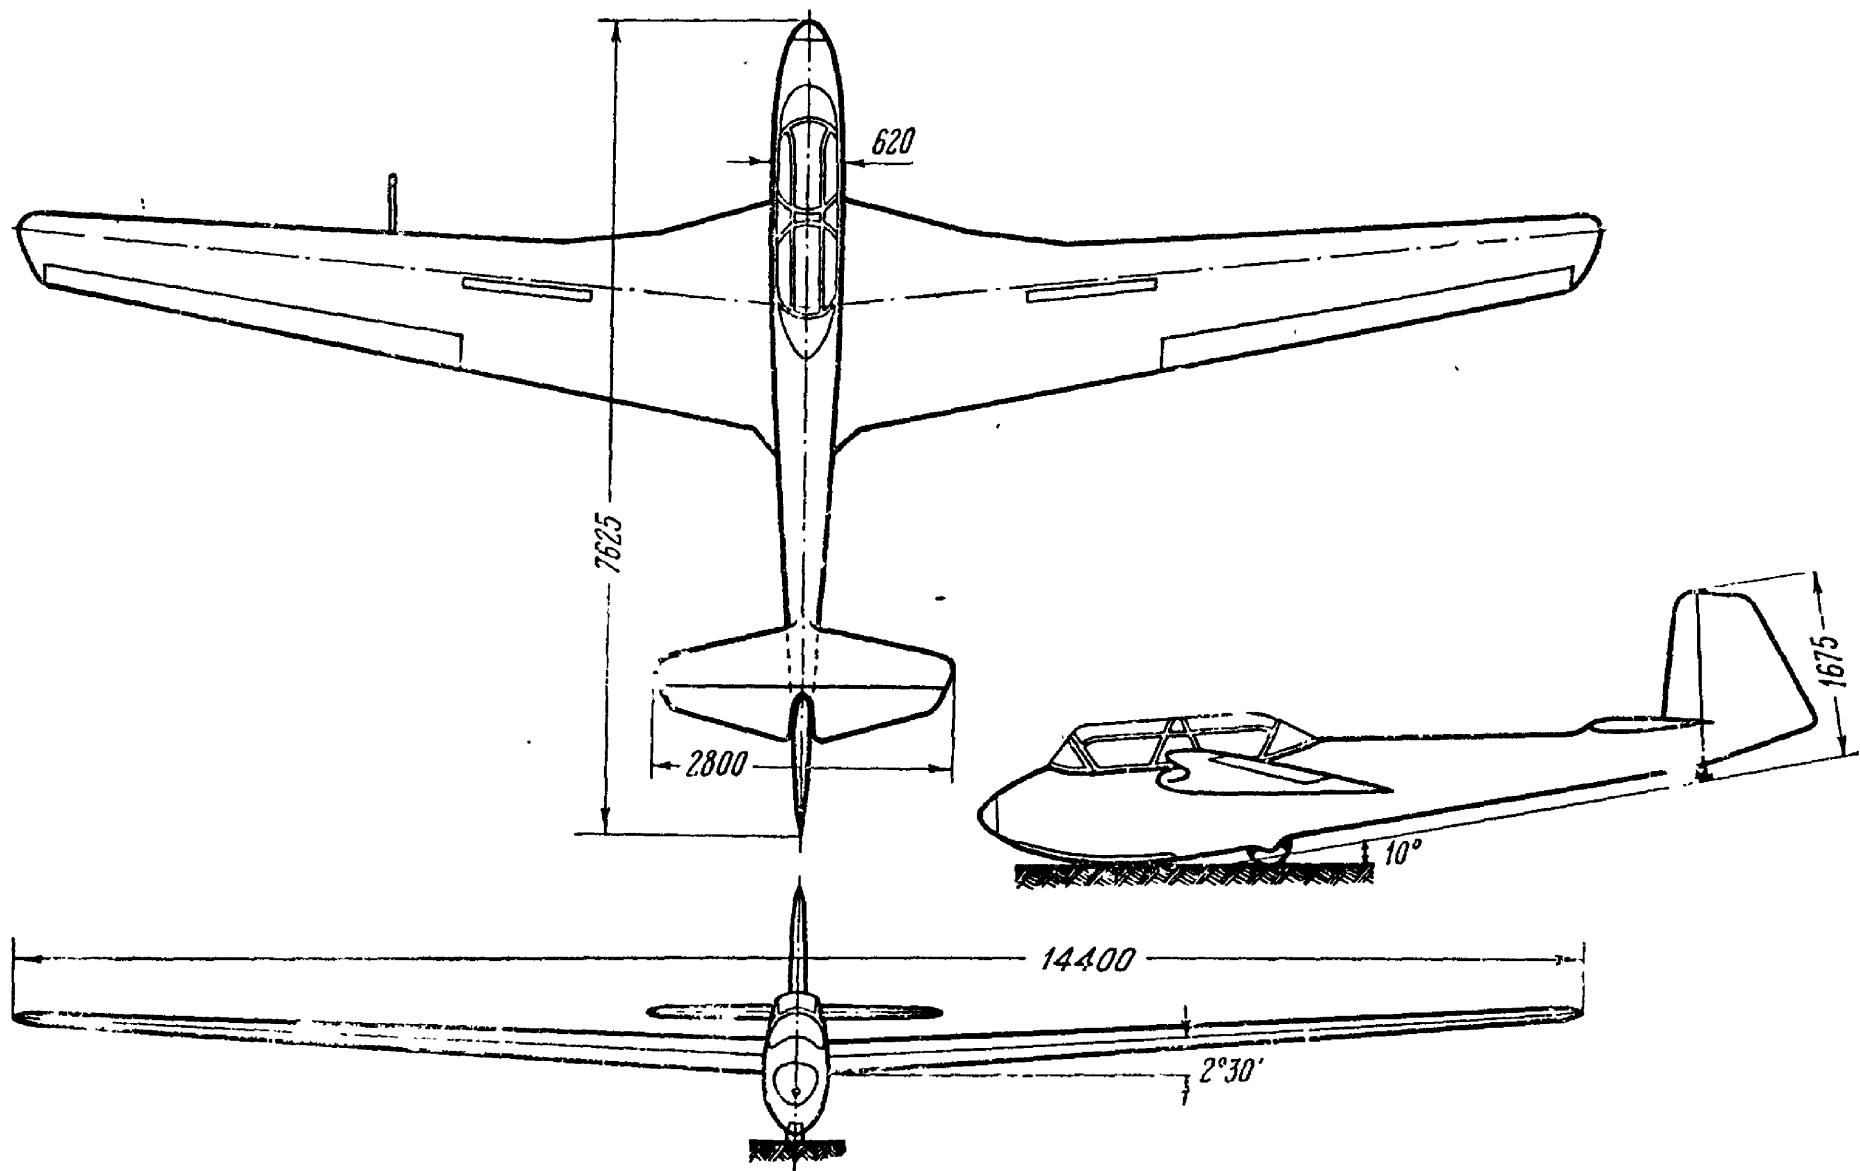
Схема двухместного планера Ш-18 конструкции Б. Н. Шереметева
